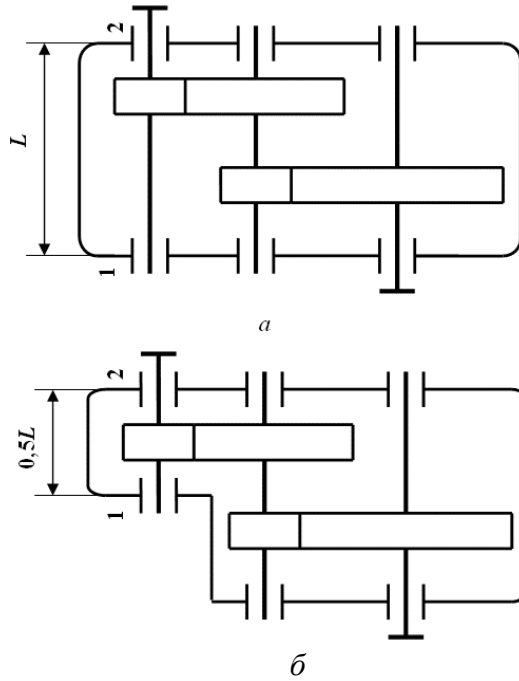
Конструктивна схема корпусу двохступеневого редуктора:
